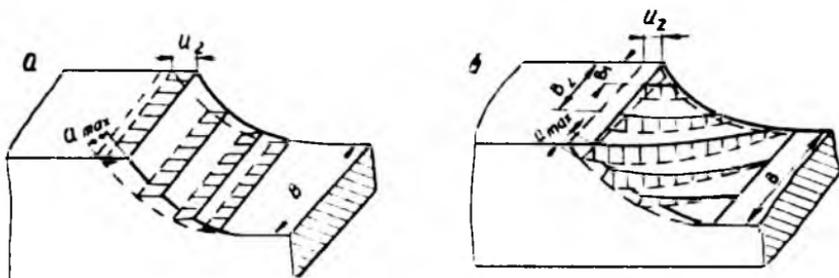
Схемы поперечного сечения стружки, снимаемой цилиндрической фрезой:
